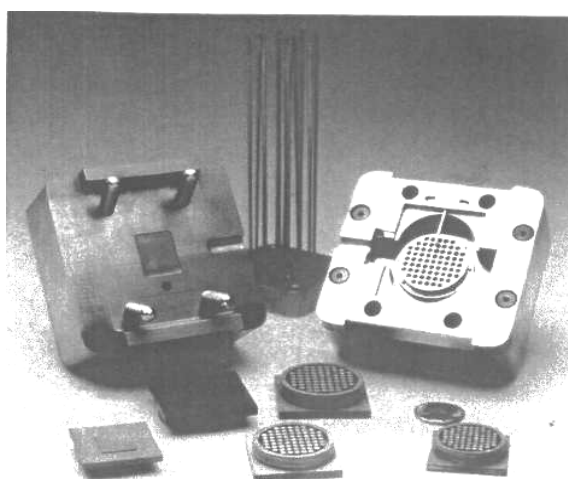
Невелика вставка з жолобками для створення зрізу вздовж шва форми
